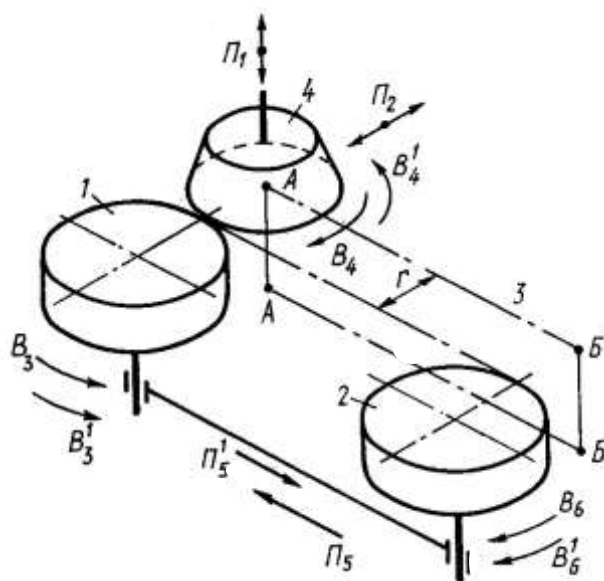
Способ последовательного зубодолбления при касательном движении врезания
